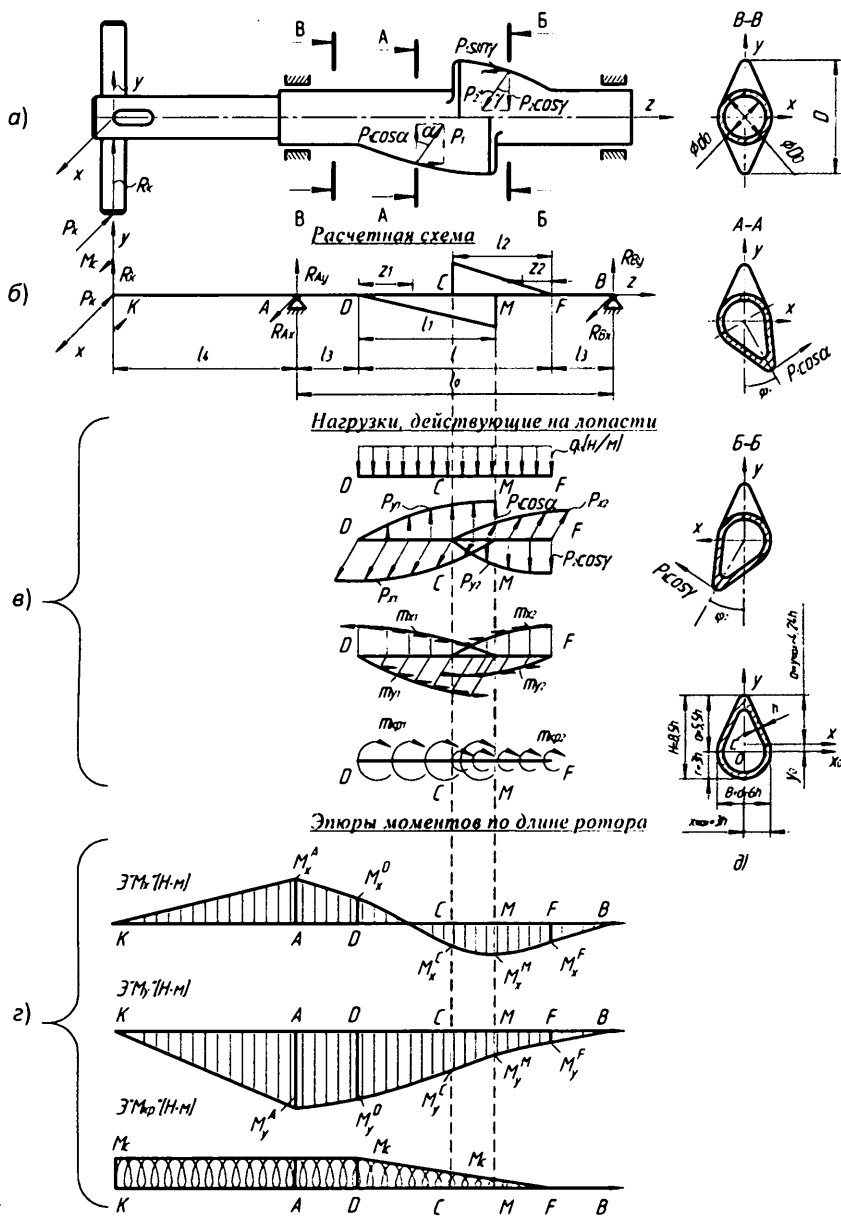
Общий вид вала ротора и его расчетная схема
